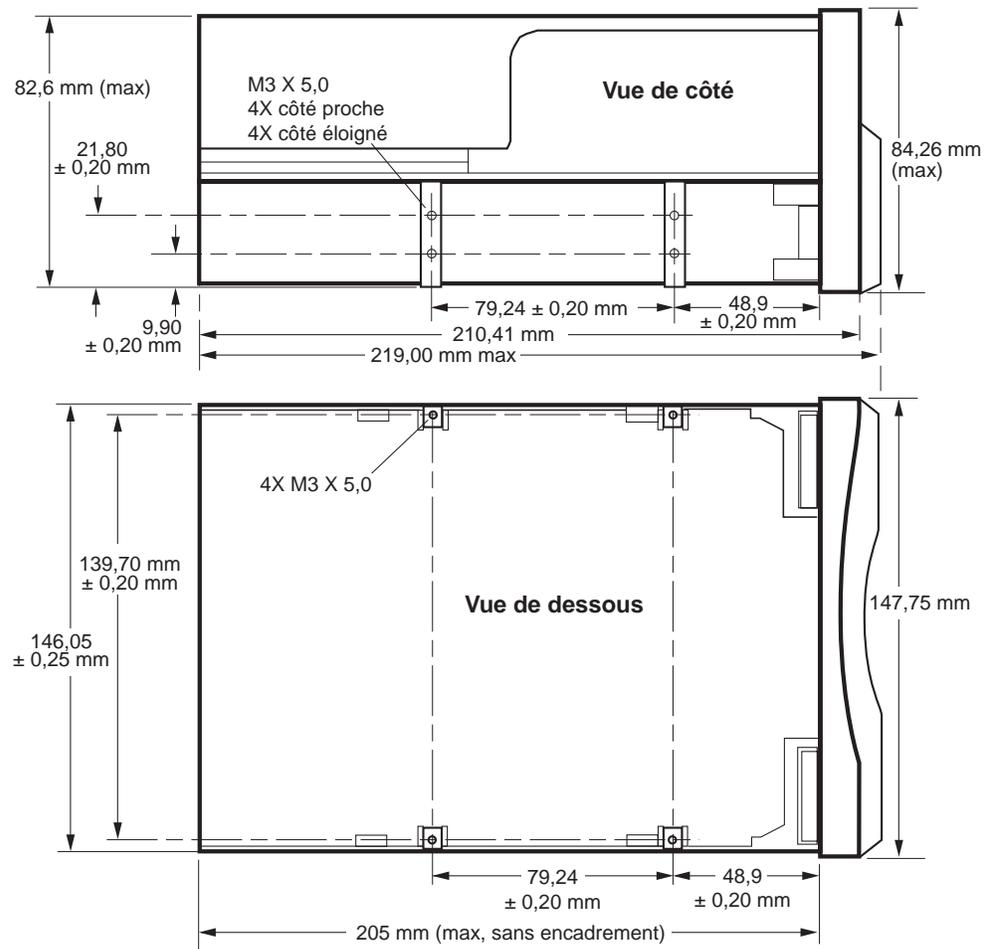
Lecteur interne Viper HVD/LVD — dimensions
